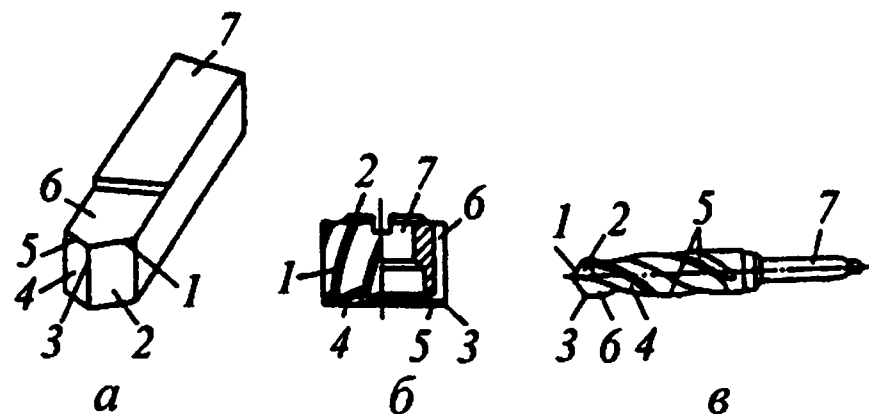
Конструкция и элементы лезвийных режущих инструментов:
